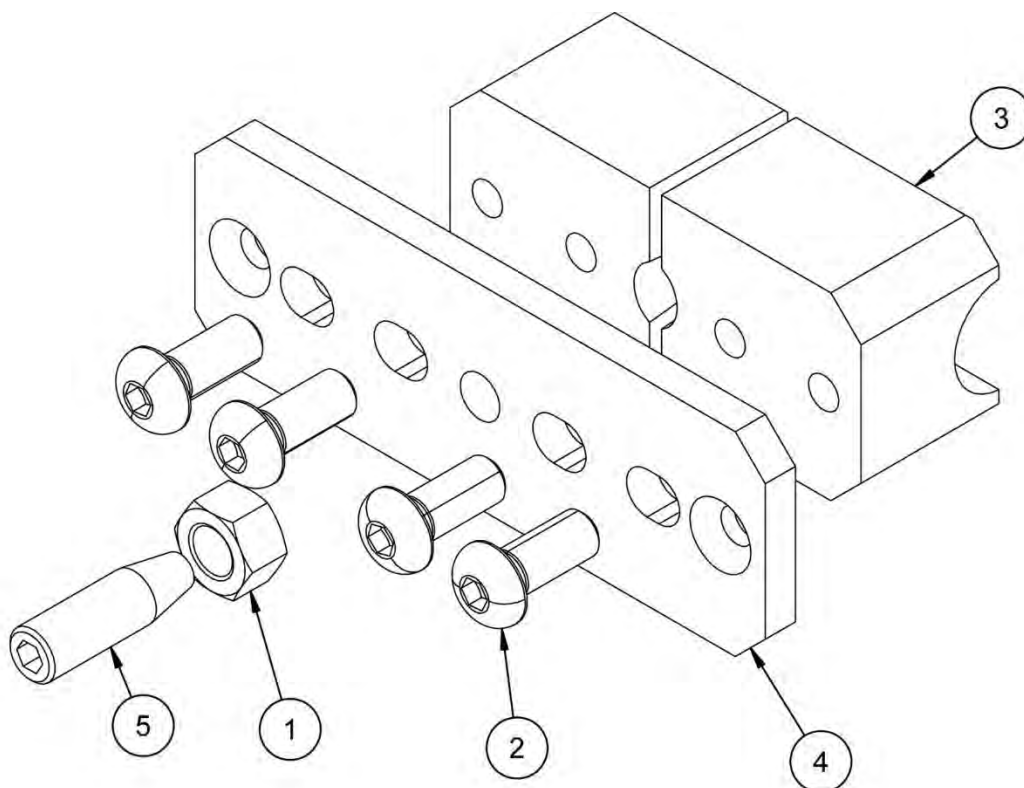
Узел поворотного привода в сборе (кат. № 15606)
